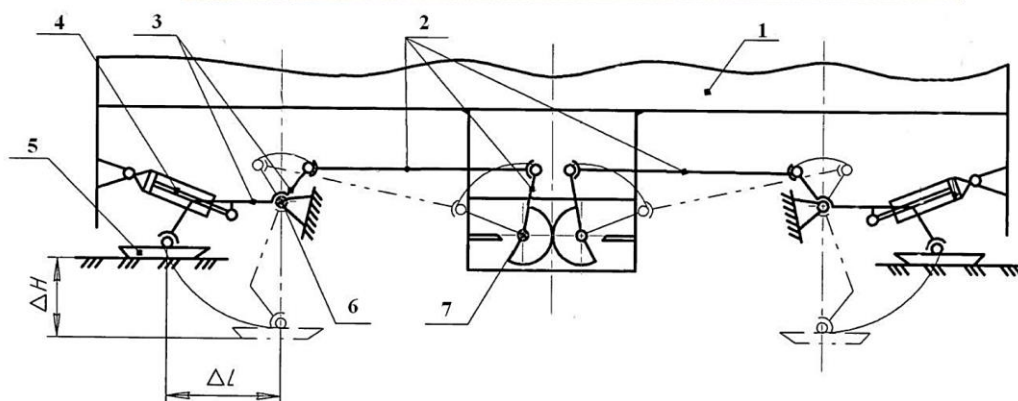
Загальний вигляд та схема механізму копіювання навішаної на комбайн очисної жниварки ЖОНТУ-6:
